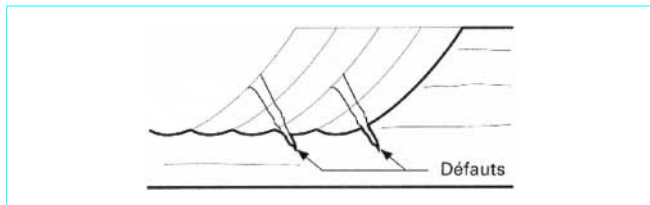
Défauts d'usinage dus à la coupe par fendage
